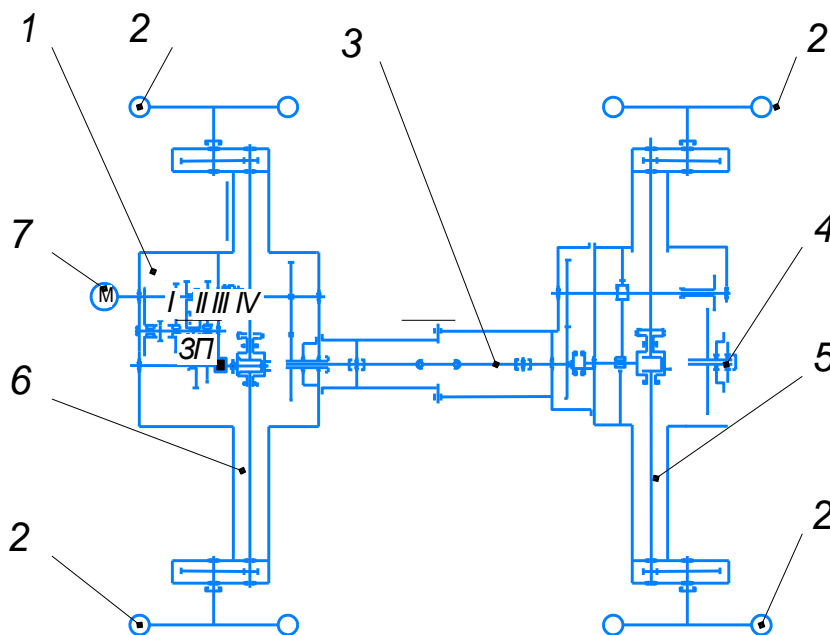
Кинематическая схема электротрактора: 1 – коробка перемены передач; 2 – шина пневматическая; 3 – карданная передача; 4 – вал отбора мощности; 5 – задняя полуось; 6 – передняя полуось; 7 – электродвигатель
